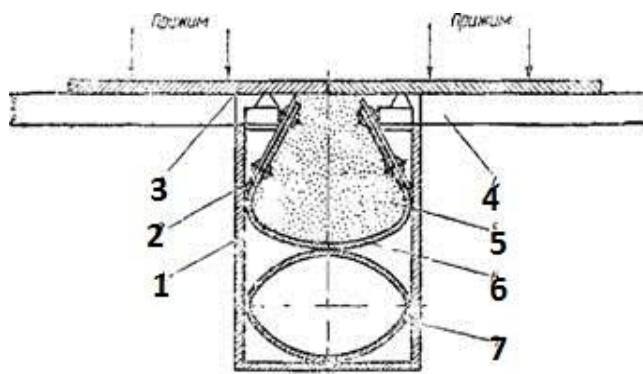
Схема приспособления для сварки на флюсовой подушке:
